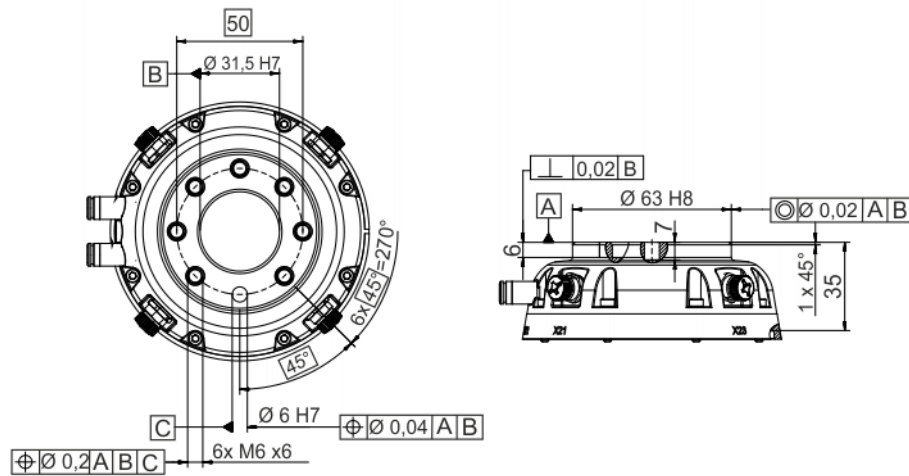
Abmessung, Medien-Flansch pneumatisch
